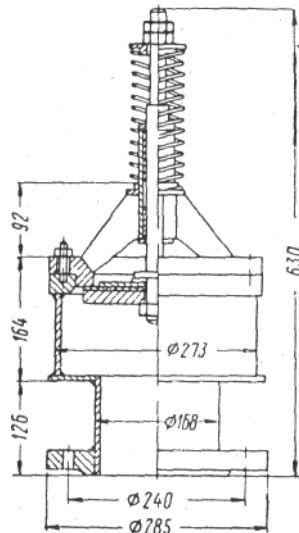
Вантуз противакуумний пружинний сталевий зварний
